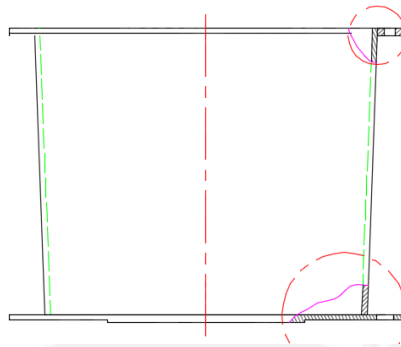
Vista de corte del cuerpo del molde cilíndrico.
